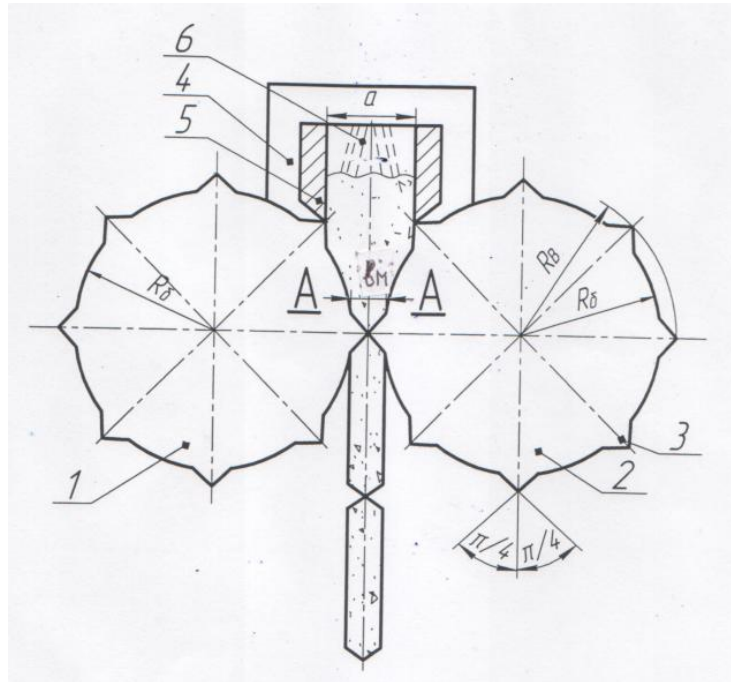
Прокатная клетка для прокатки порошковых композиций
